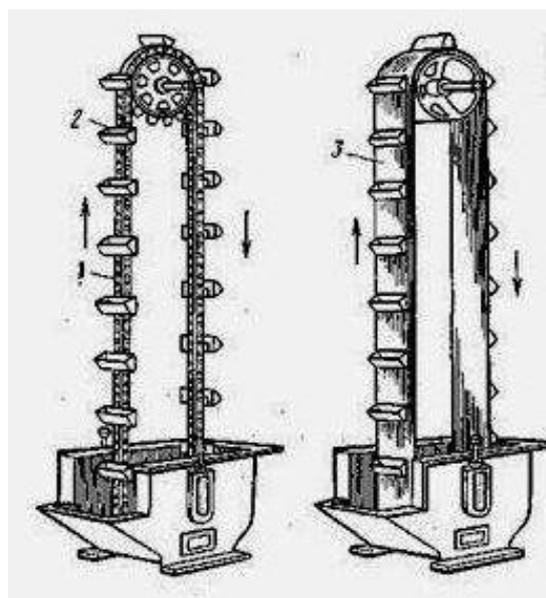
Элеваторы: 1 - цепь, 2 - ковш, 3 - лента
